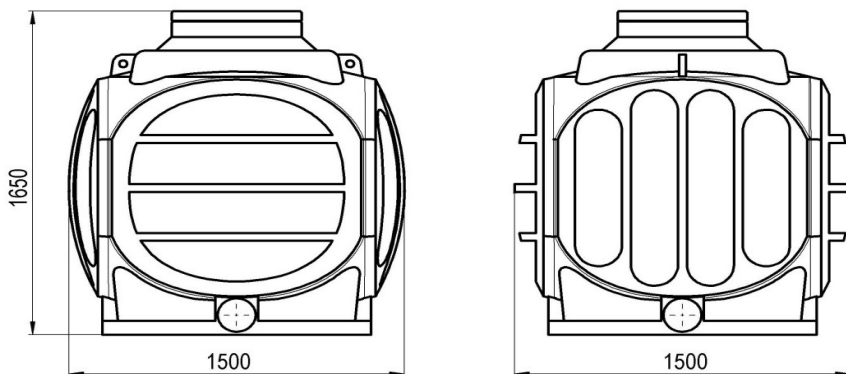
Колодец ККП-4-ССД в сборе, вид сбоку, габаритные размеры
